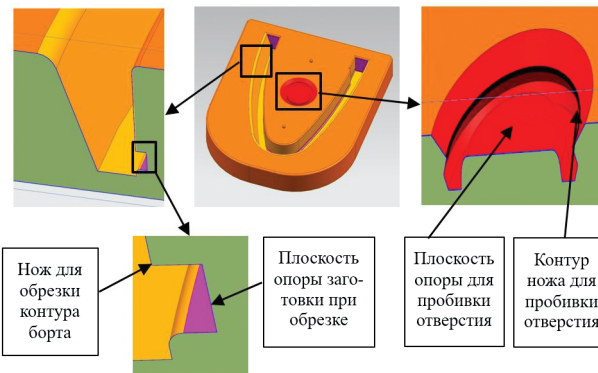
Оснастка для формoобразования и обрезки борта и отбортовки
